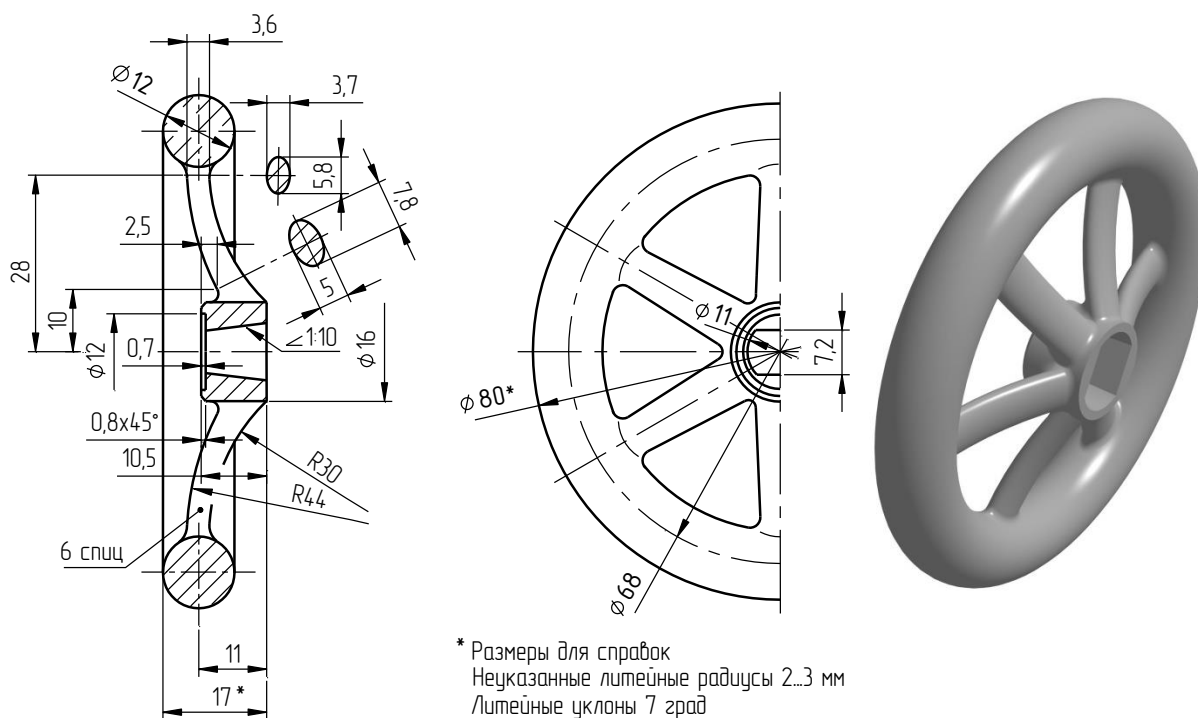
Чертеж детали (маховичка вентиля), в котором вид оборван по оси симметрии – сокращен
